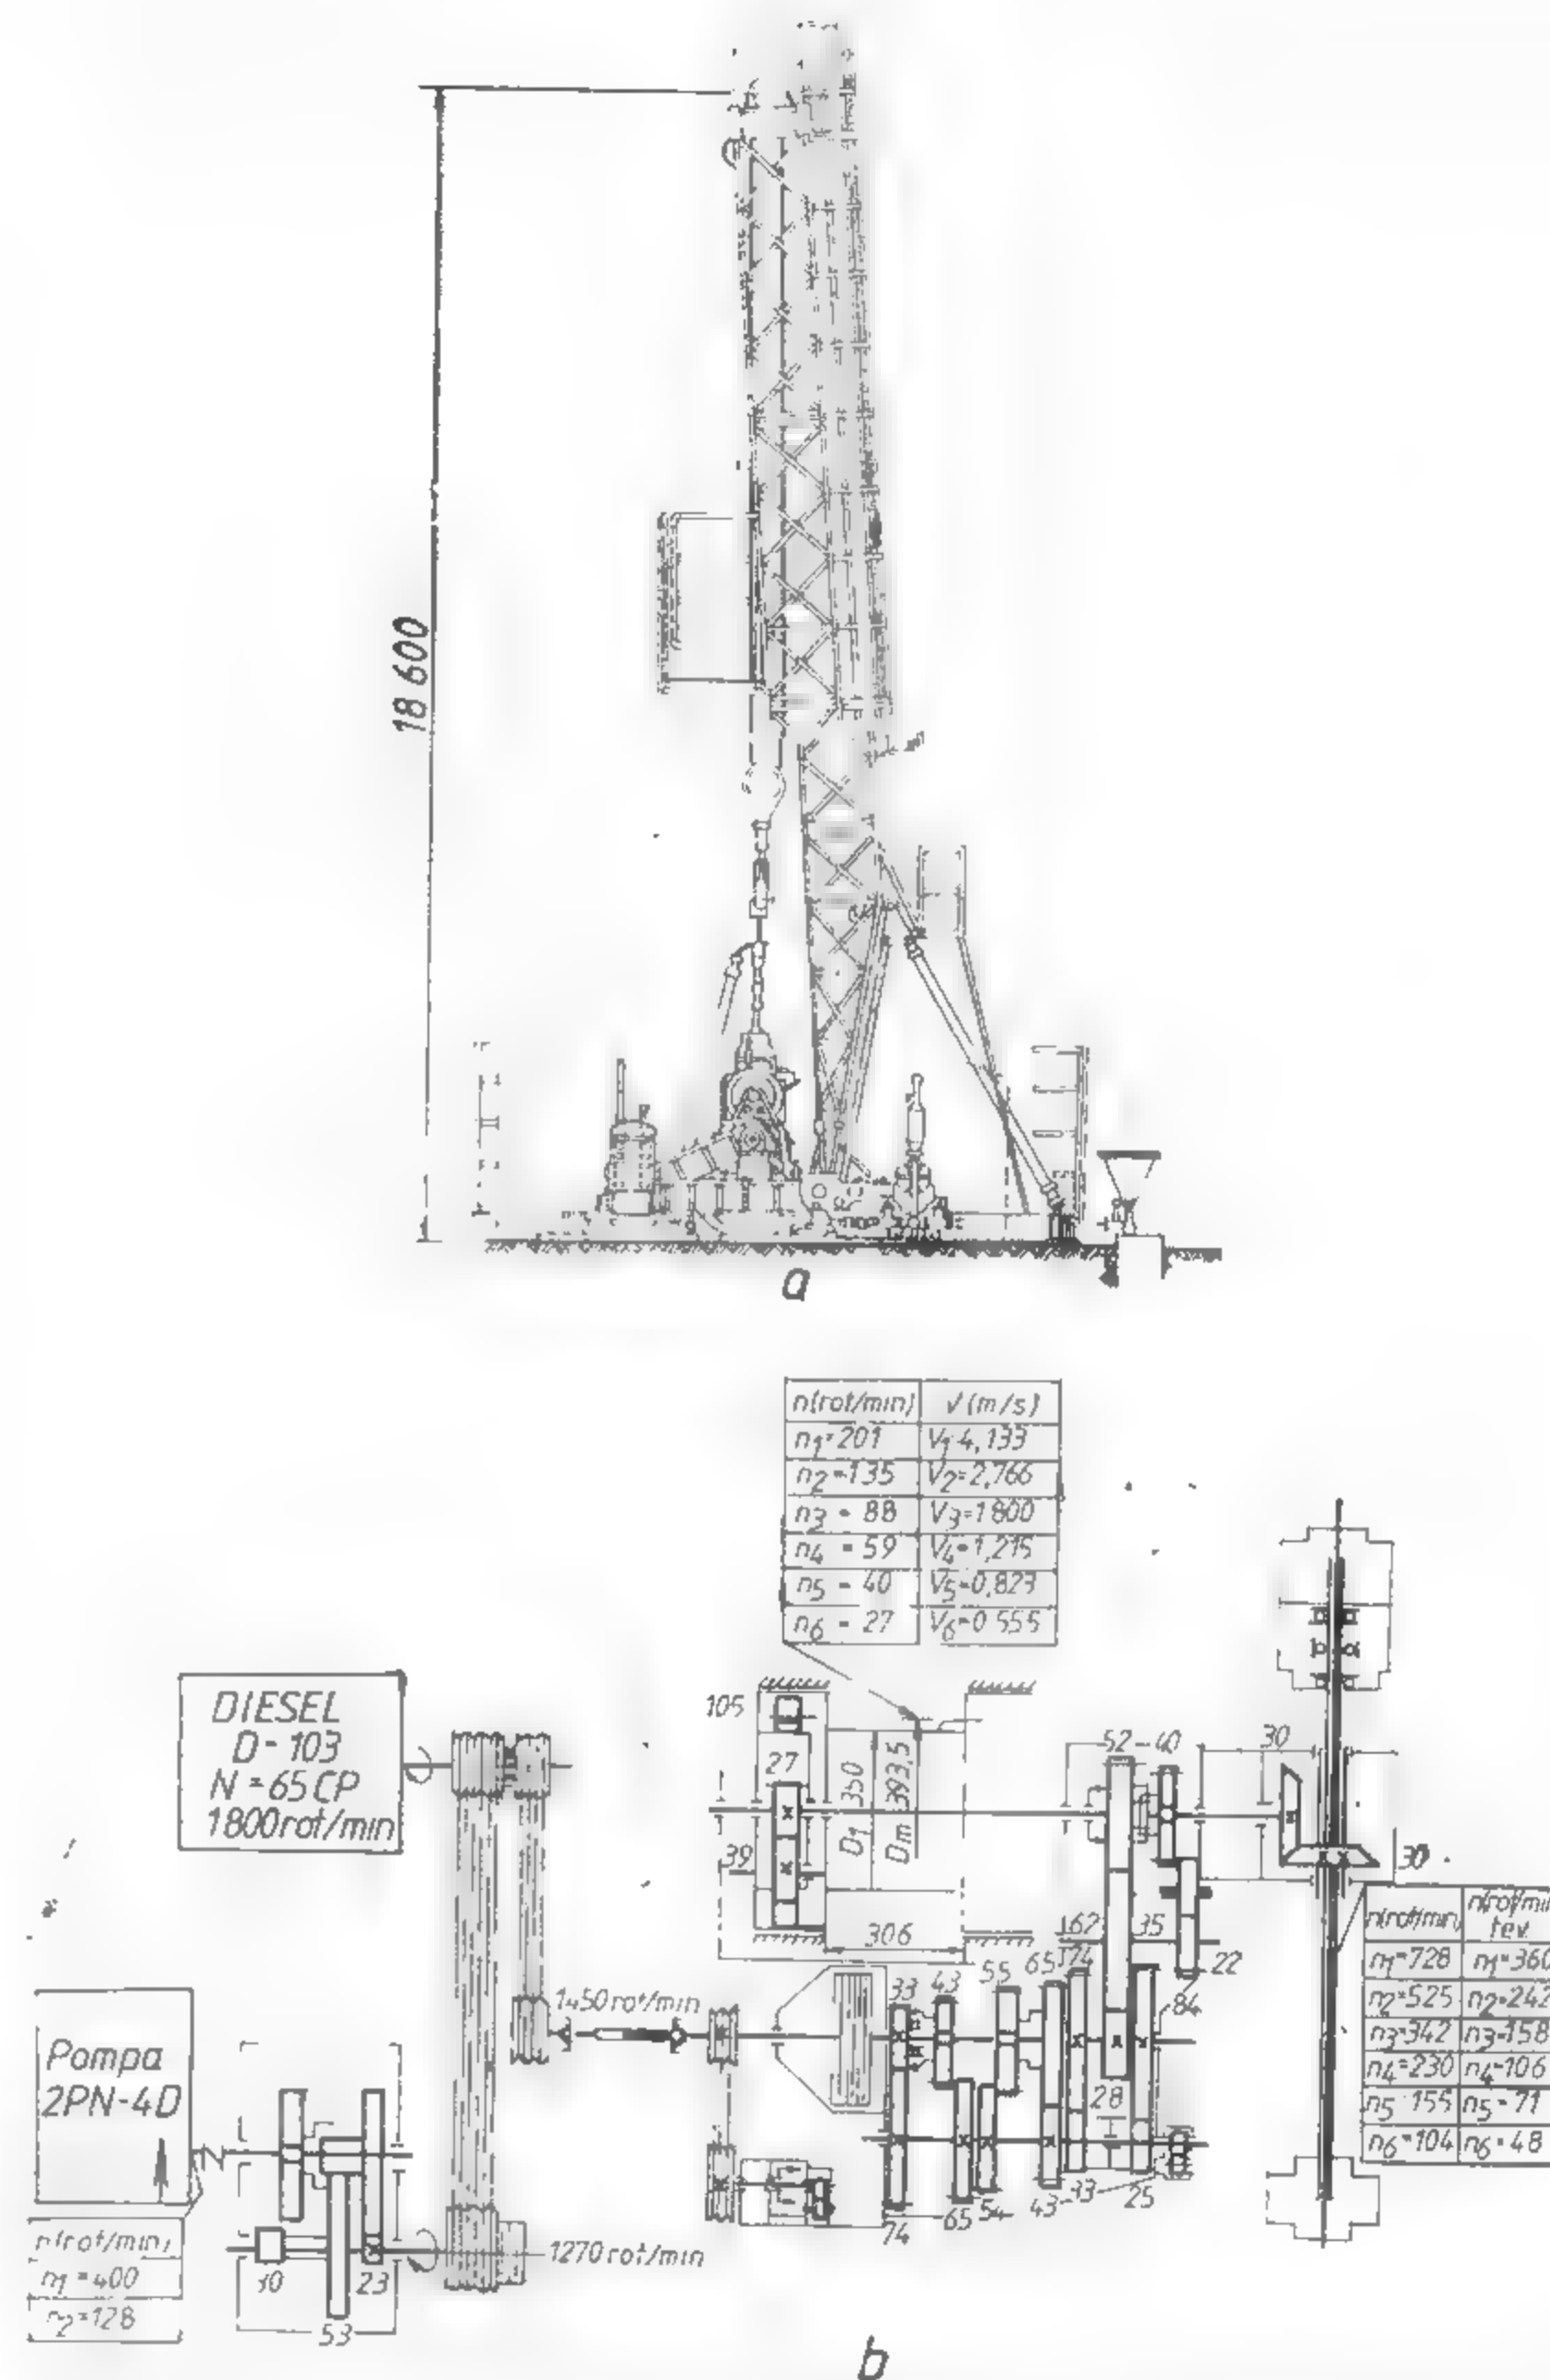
Instalație SG-650 acționată cu motor Diesel (varianta I):
